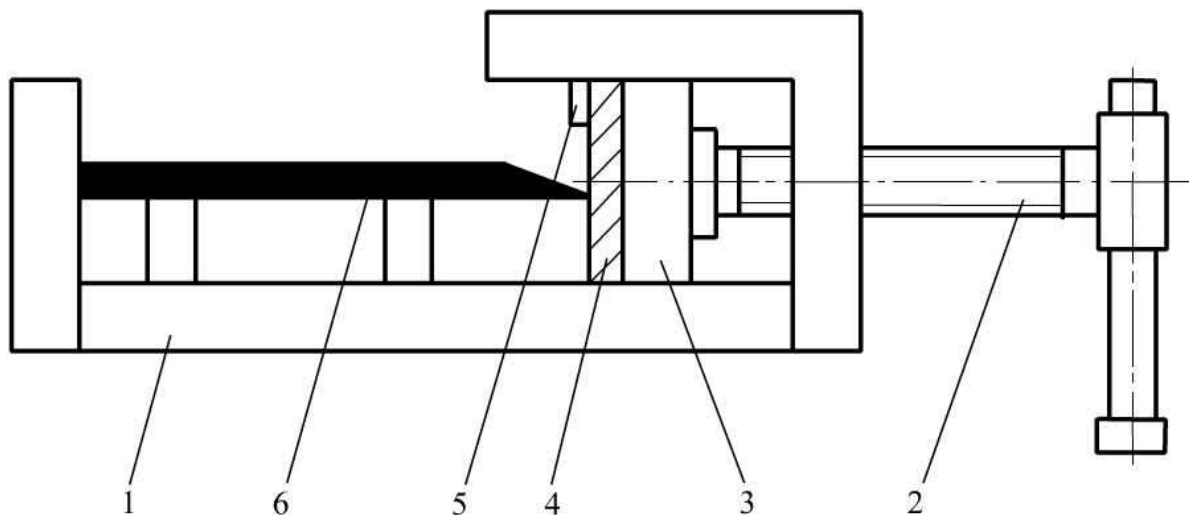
Схема пристосування для зняття відбитків з лез ґрунторізальних елементів: 1-корпус; 2-гвинт; 3-повзун; 4-свинцева пластина; 5-скоба; 6-зразок
